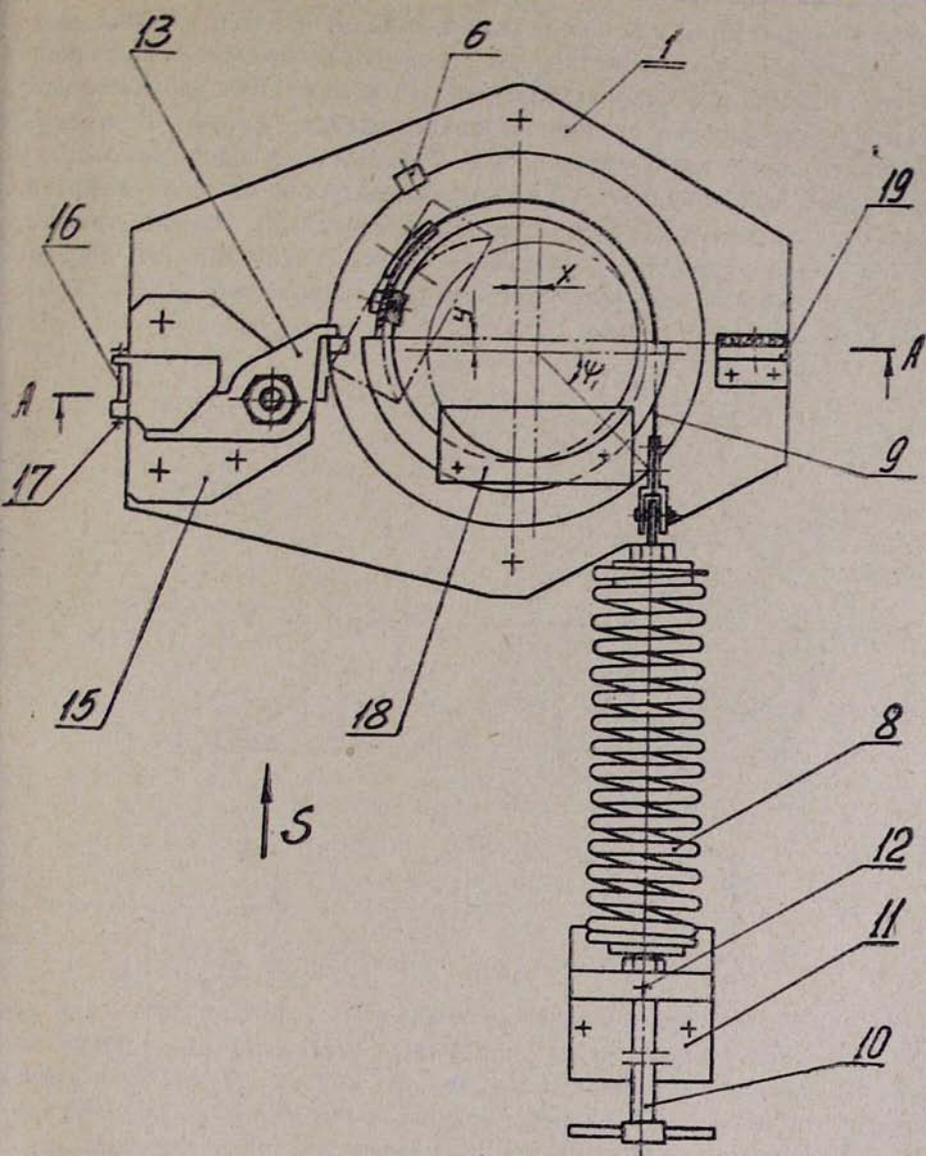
Приспособление для получения корня стружки при фрезеровании.
